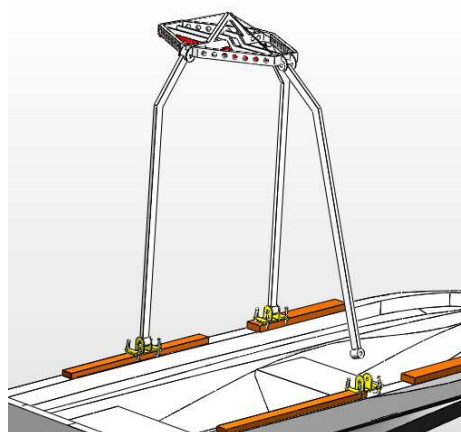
Estrutura de suporte elevada - proposta descartada.
